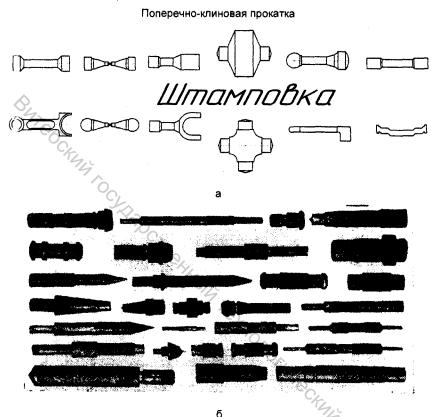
Изделия, полученные поперечно-клиновой прокаткой для последующей штамповки (а) и механической обработки (б)
